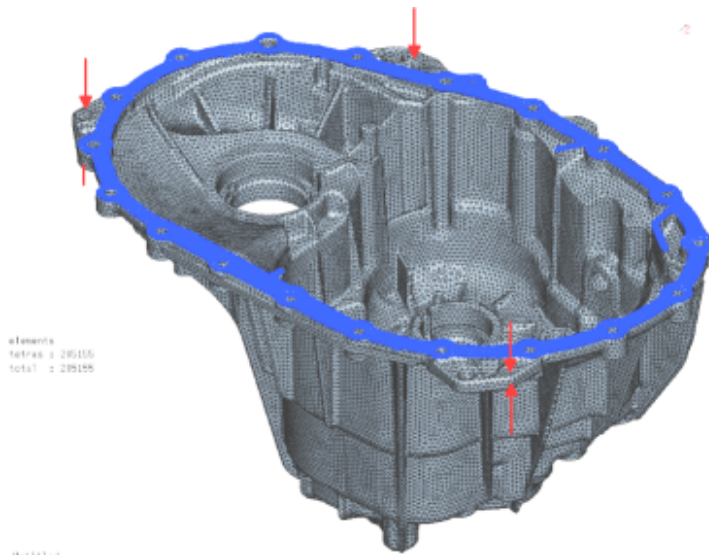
Prise de pièce. La surface usinée est repérée en bleu.
